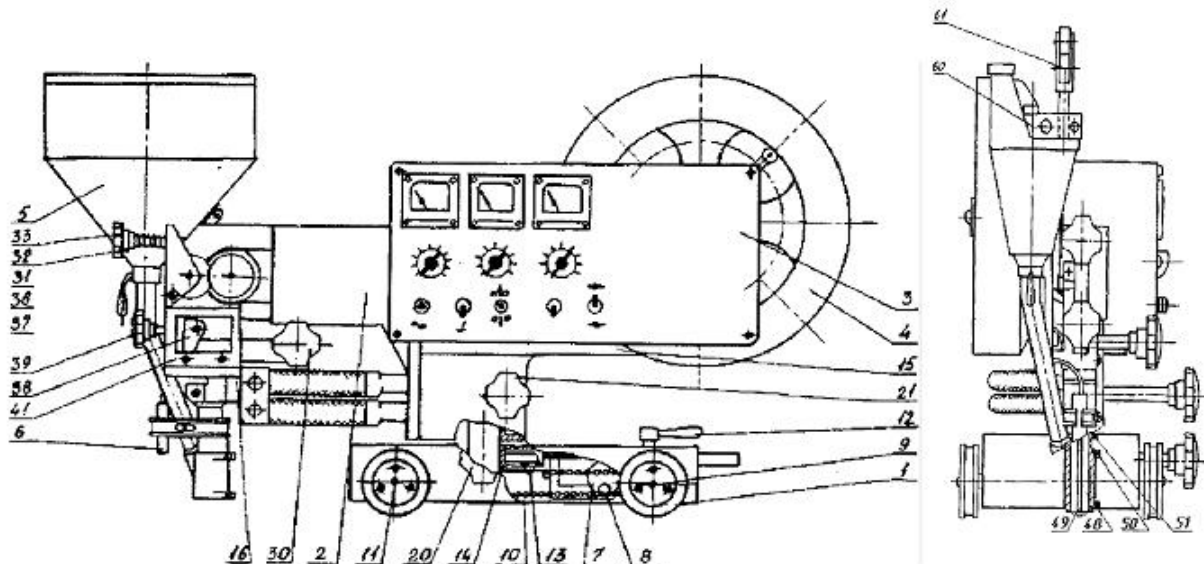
Зовнішній вид трактора АДФ-1001
